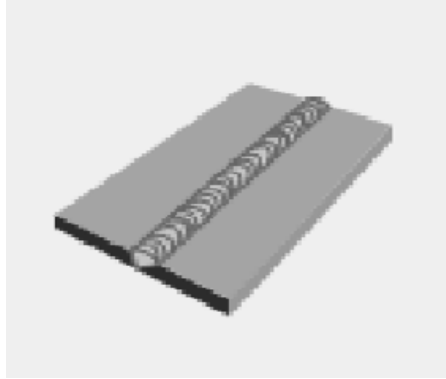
Soldadura de penetración completa. (Nuñez, 2012)
